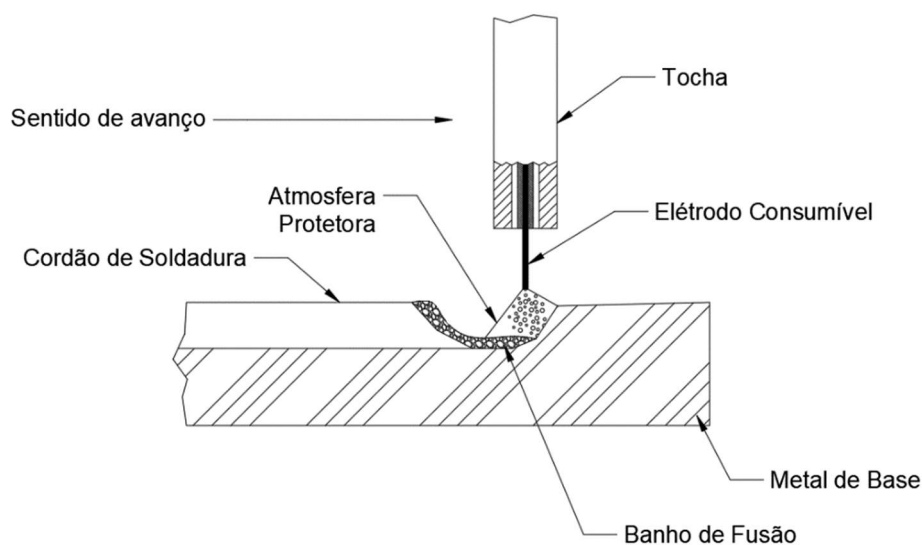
Ilustração esquemática do processo de soldadura MIG.
